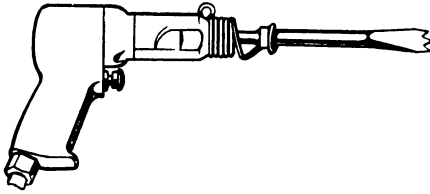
Пневматический молоток с «перкой» (резаком) для резки листового металла
